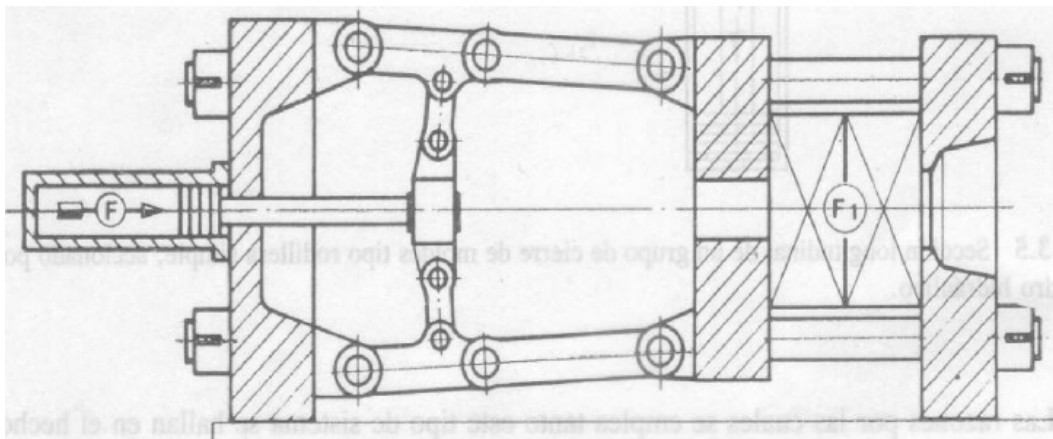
Cierre por rodillero doble con 5 puntos de unión.
